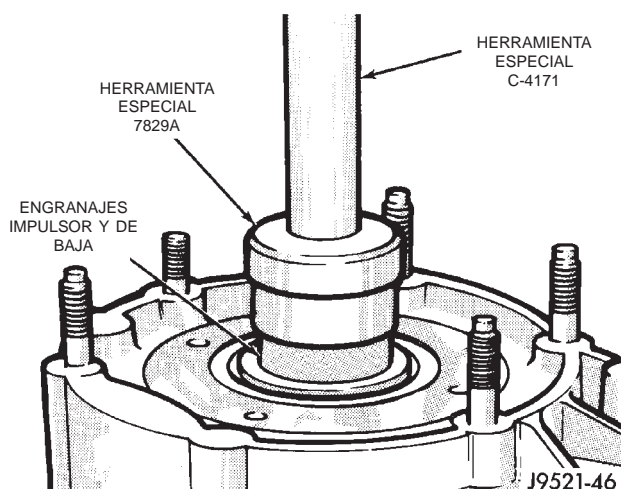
Desmontaje del conjunto de engranaje impulsor y de baja
